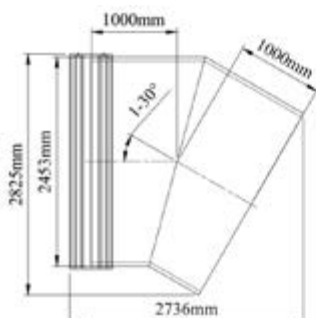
Cot GRP/PAFSIN DN 2400, 1 - 30°
